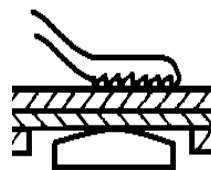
Зубчатая рейка, расположенная сверху материала зубьями вниз
